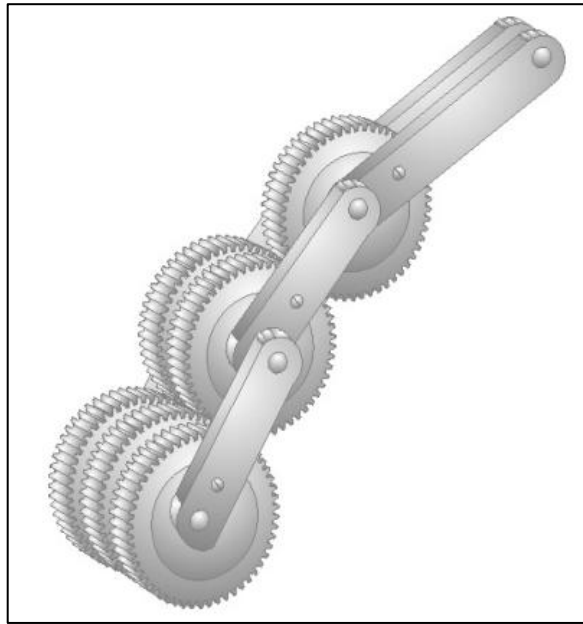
Mecanismo de um dedo utilizando engrenagens cilíndricas.
